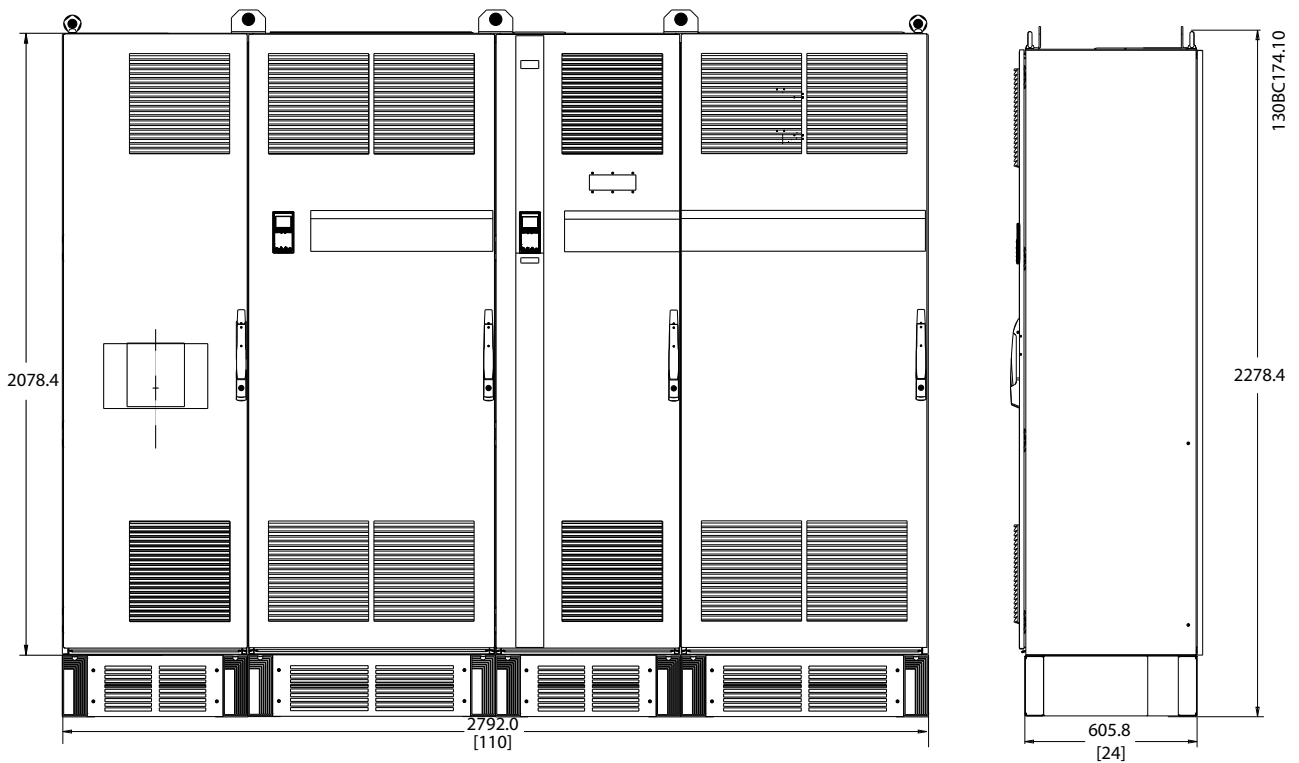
Framegrootte F18, voor- en zijaanzicht
